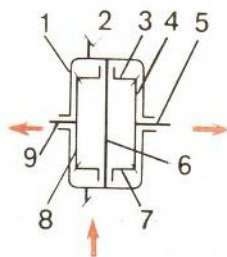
Схема простого дифференциала с коническими зубчатыми колесами:
